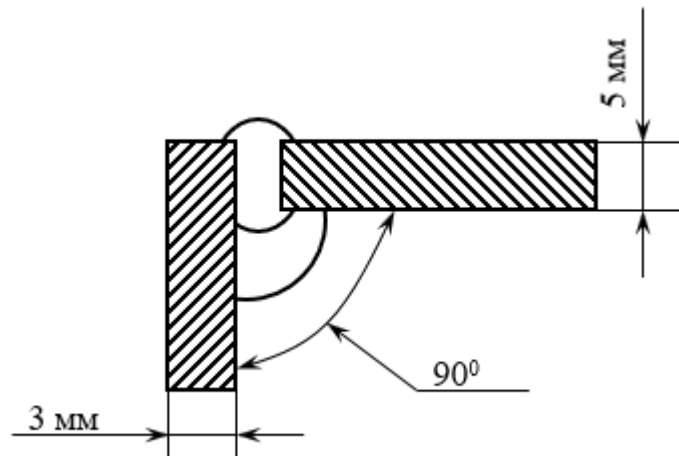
Схема підготовлених країв зварювальних деталей
